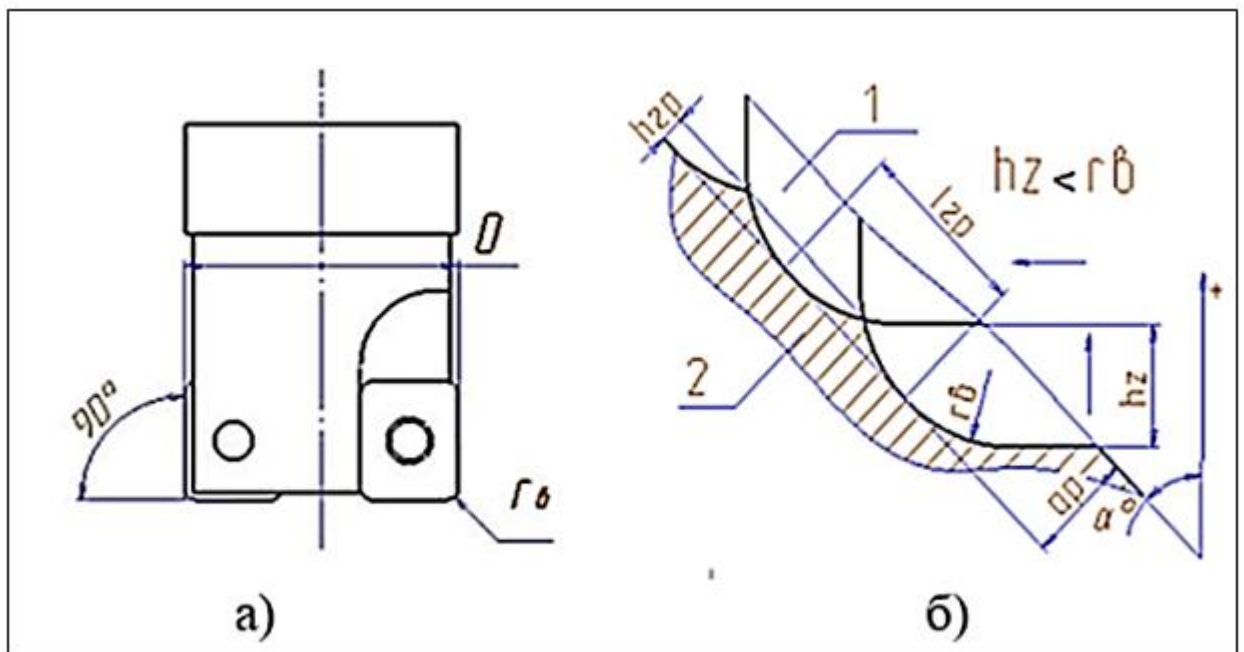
Концевая фреза, оснащенная НТП (а) и компьютерная модель зоны контакта фрезы и обрабатываемой поверхности при послойном 2.5 координатном фрезеровании наклонной плоскости (б): 1 – режущий инструмент; 2 – заготовка
